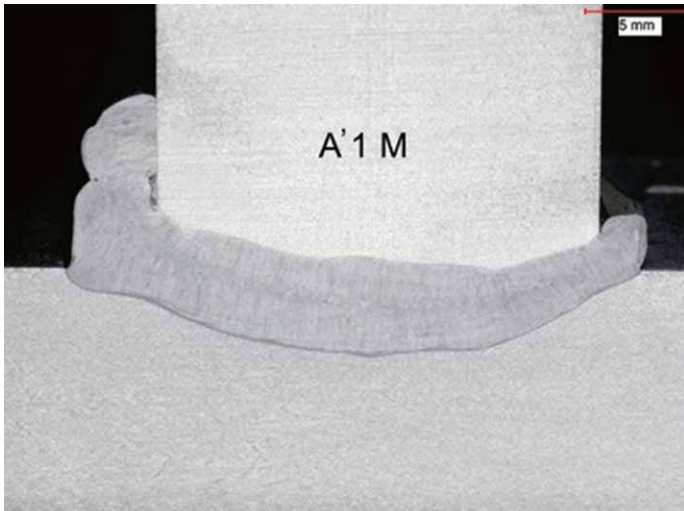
Makroschliff einer einwandfreien Bolzenschweißung (© Trillmich)
